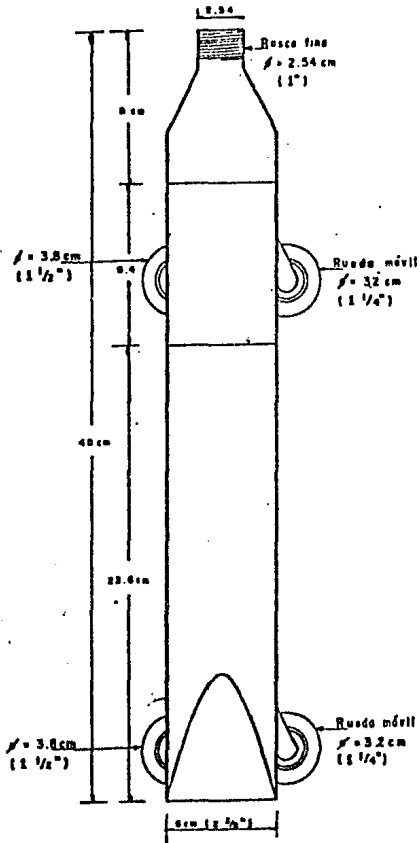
a Detalles de Instrumentación tipo "A". CORTE B-B'
